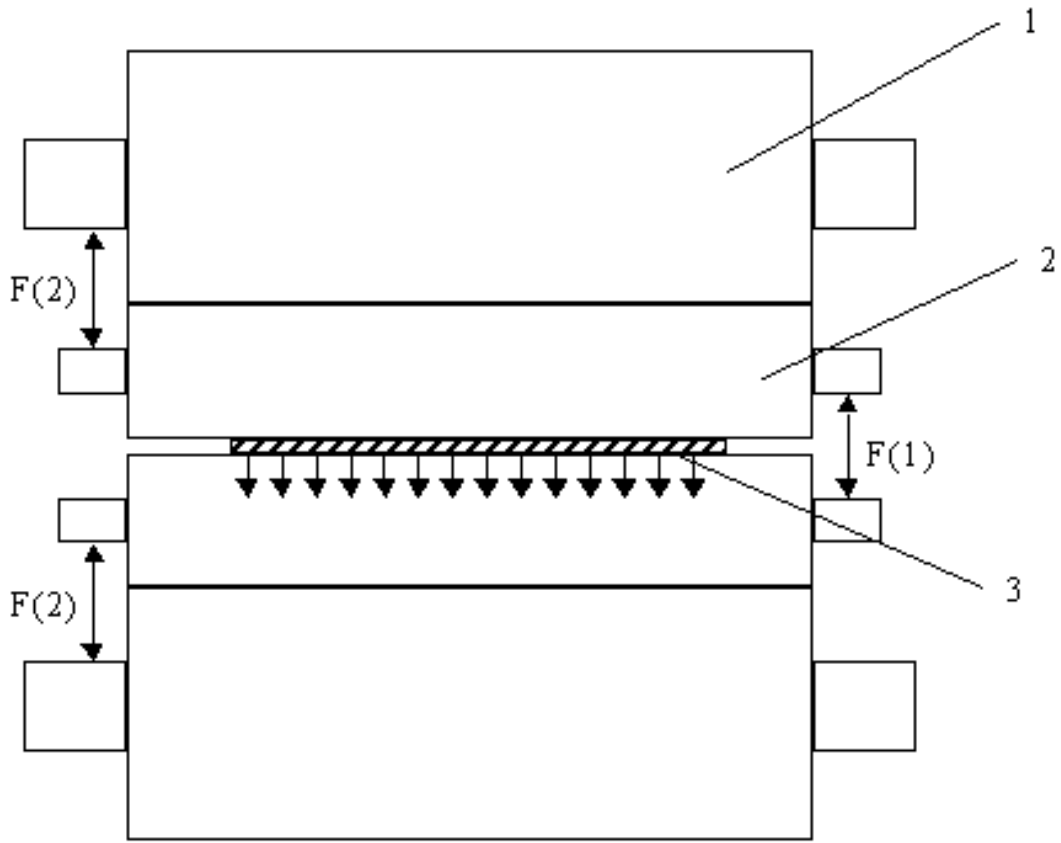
Схема здійснення гідровигину робочих валків: 1 - вал опорний; 2- вал робочий; 3- штаби;  $F(1)$  - гідровигин робочих валків;  $F(2)$  - додатковий вигин робочих валків.
